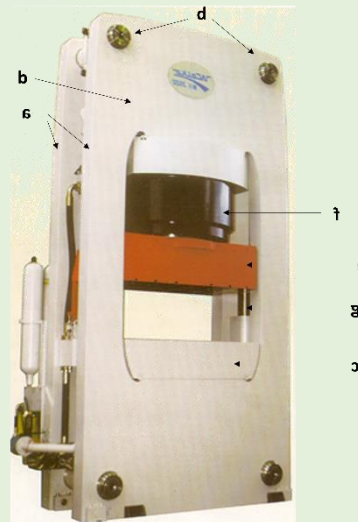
Estructura de láminas de las prensas WELKO, serie WK y grupo de prensado.
